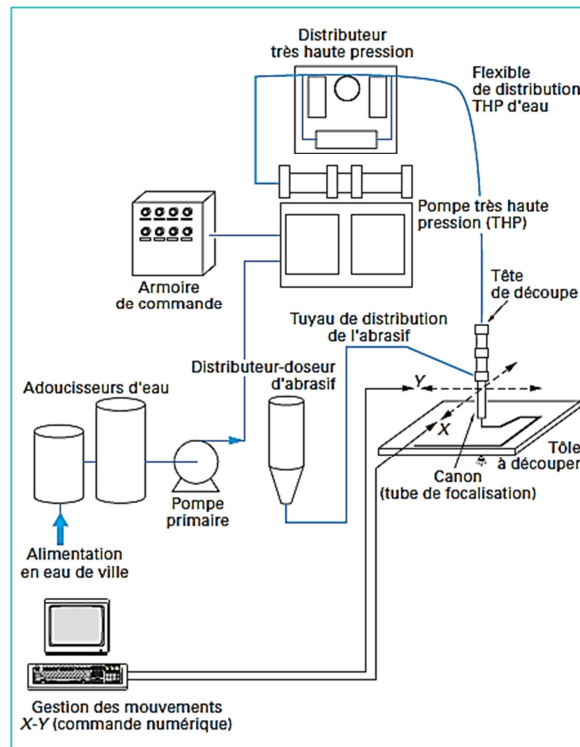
Schéma de principe d'une installation de coupe au jet d'eau
